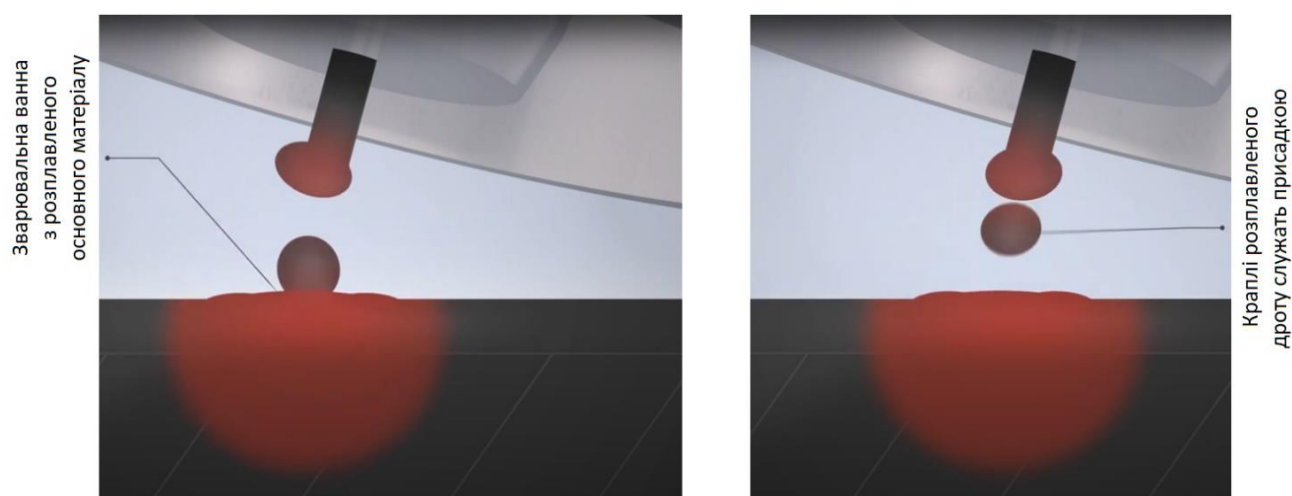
Формування зварювальної ванни та перенесення розплавленого дроту
